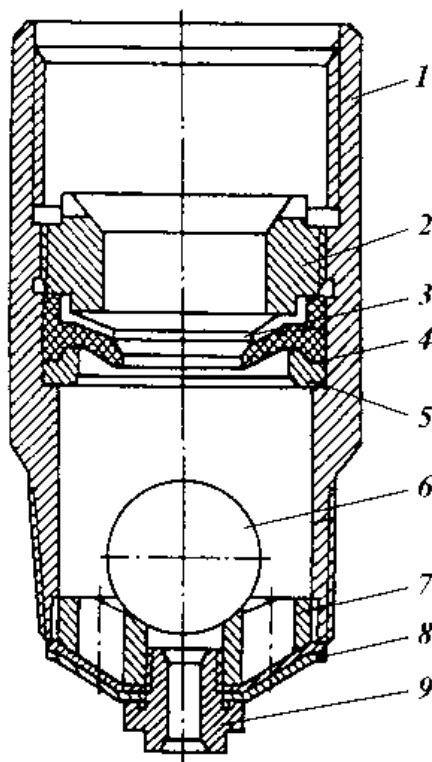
Клапан обратный дроссельный. 1-корпус; 2-нажимная гайка; 3-набор резиновых шайб; 4-резиновая диафрагма; 5-опорное кольцо; 6-шар; 7-ограничительное кольцо; 8-резинотканевая мембрана; 9-дроссель.
